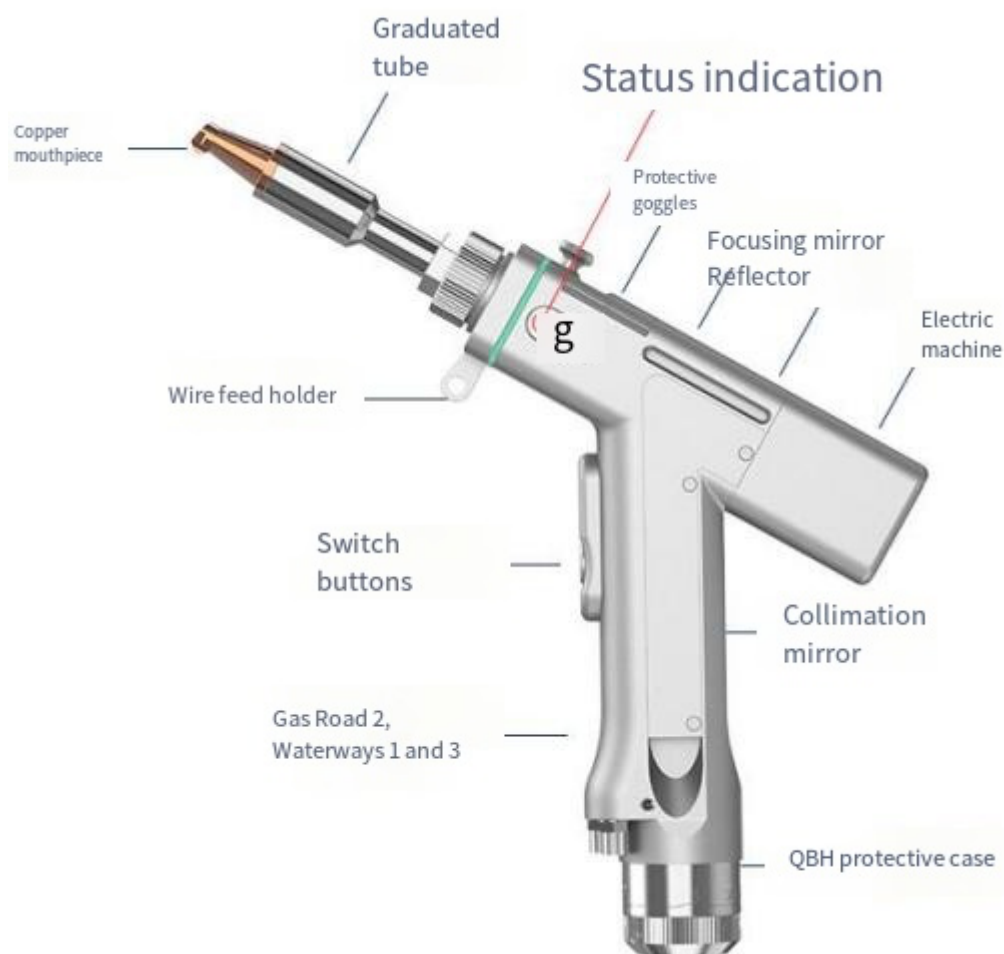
Diagrama esquemático del cabezal de soldadura SUP-23T
